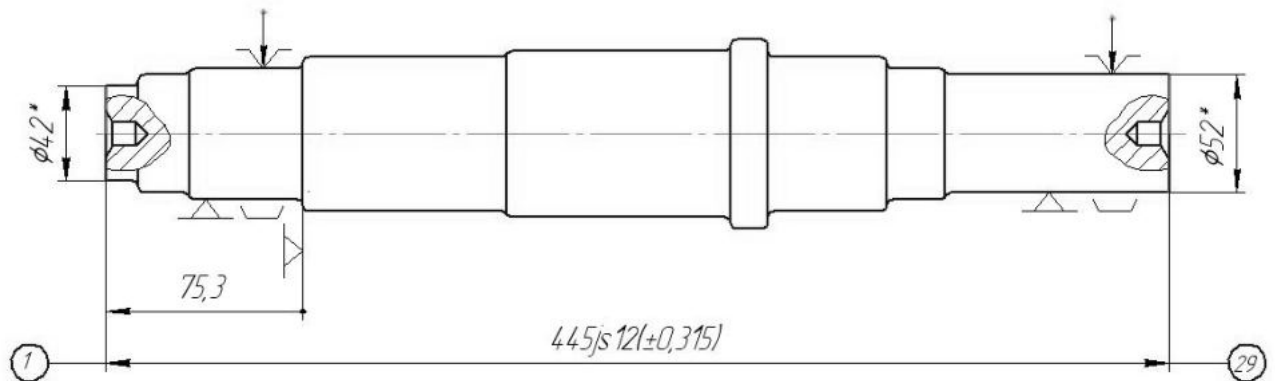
Операційний ескіз фрезерно-центрувальної операції 010
